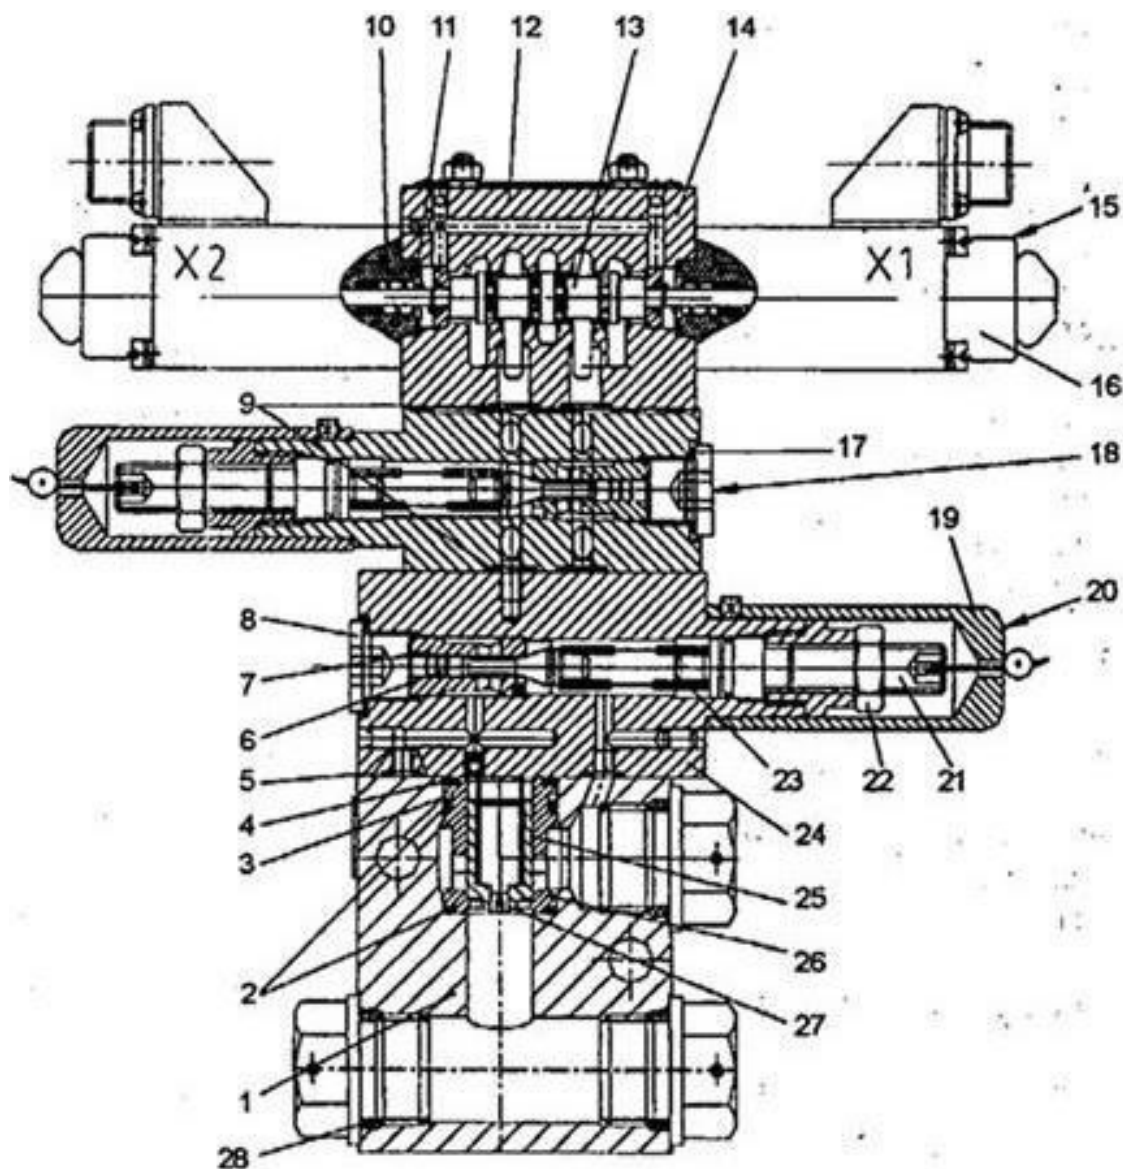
Блок разгрузочно-предохранительный:
